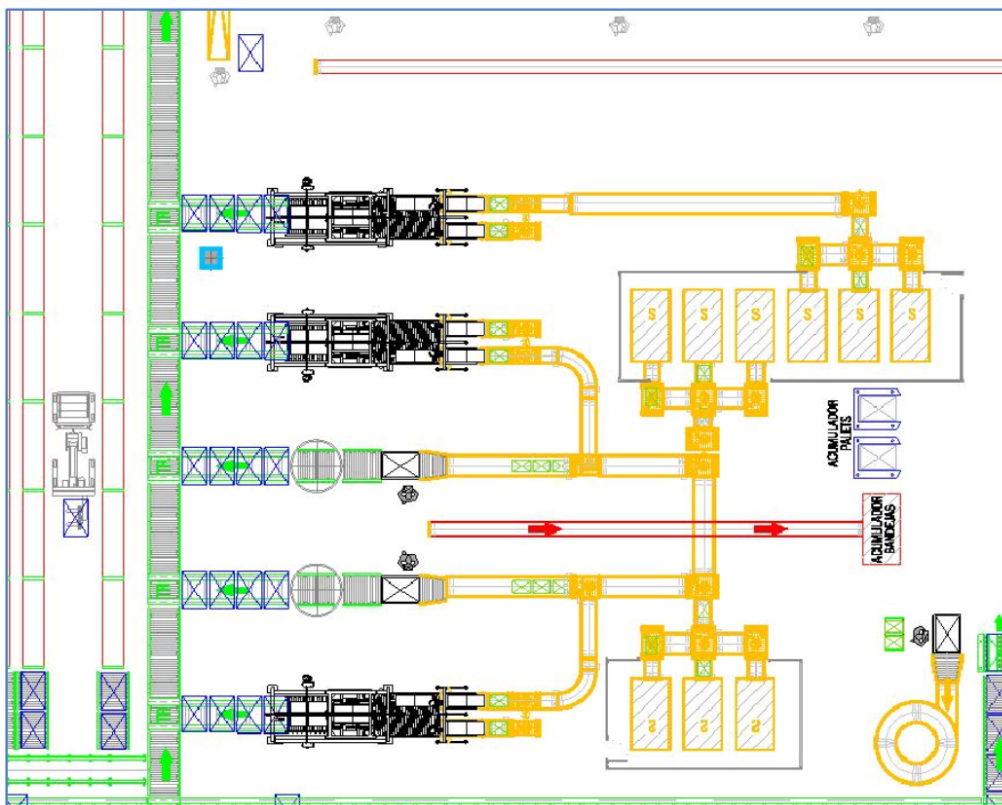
Detalle área paletizado escenario automático Fuente Elaboración propia
